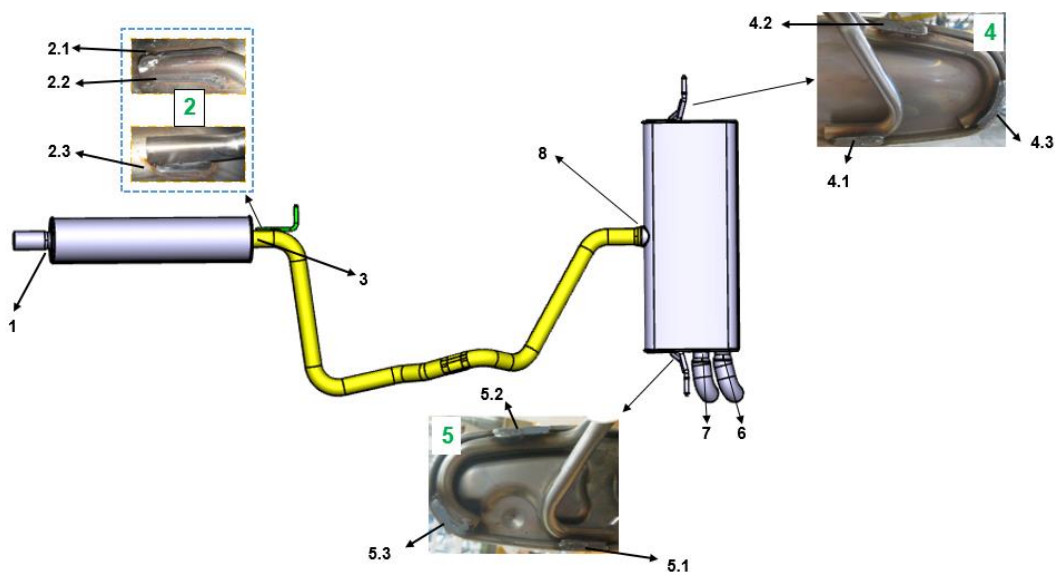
Pontos de soldadura de um sistema de escape numerados
